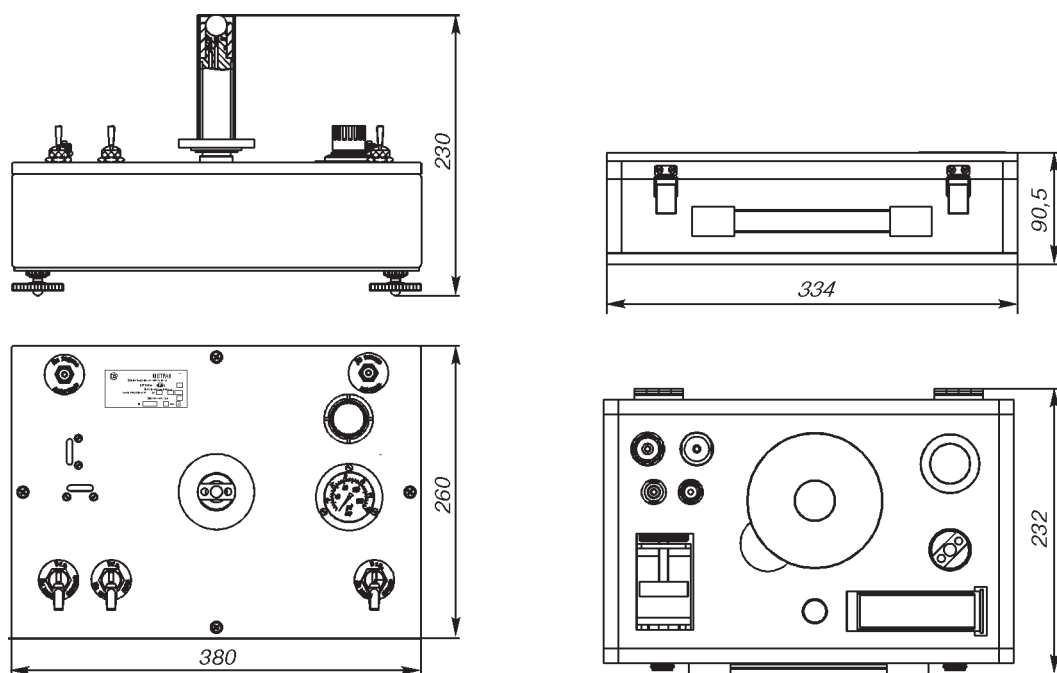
Калибратор давления пневматический 504 Воздух-I.
